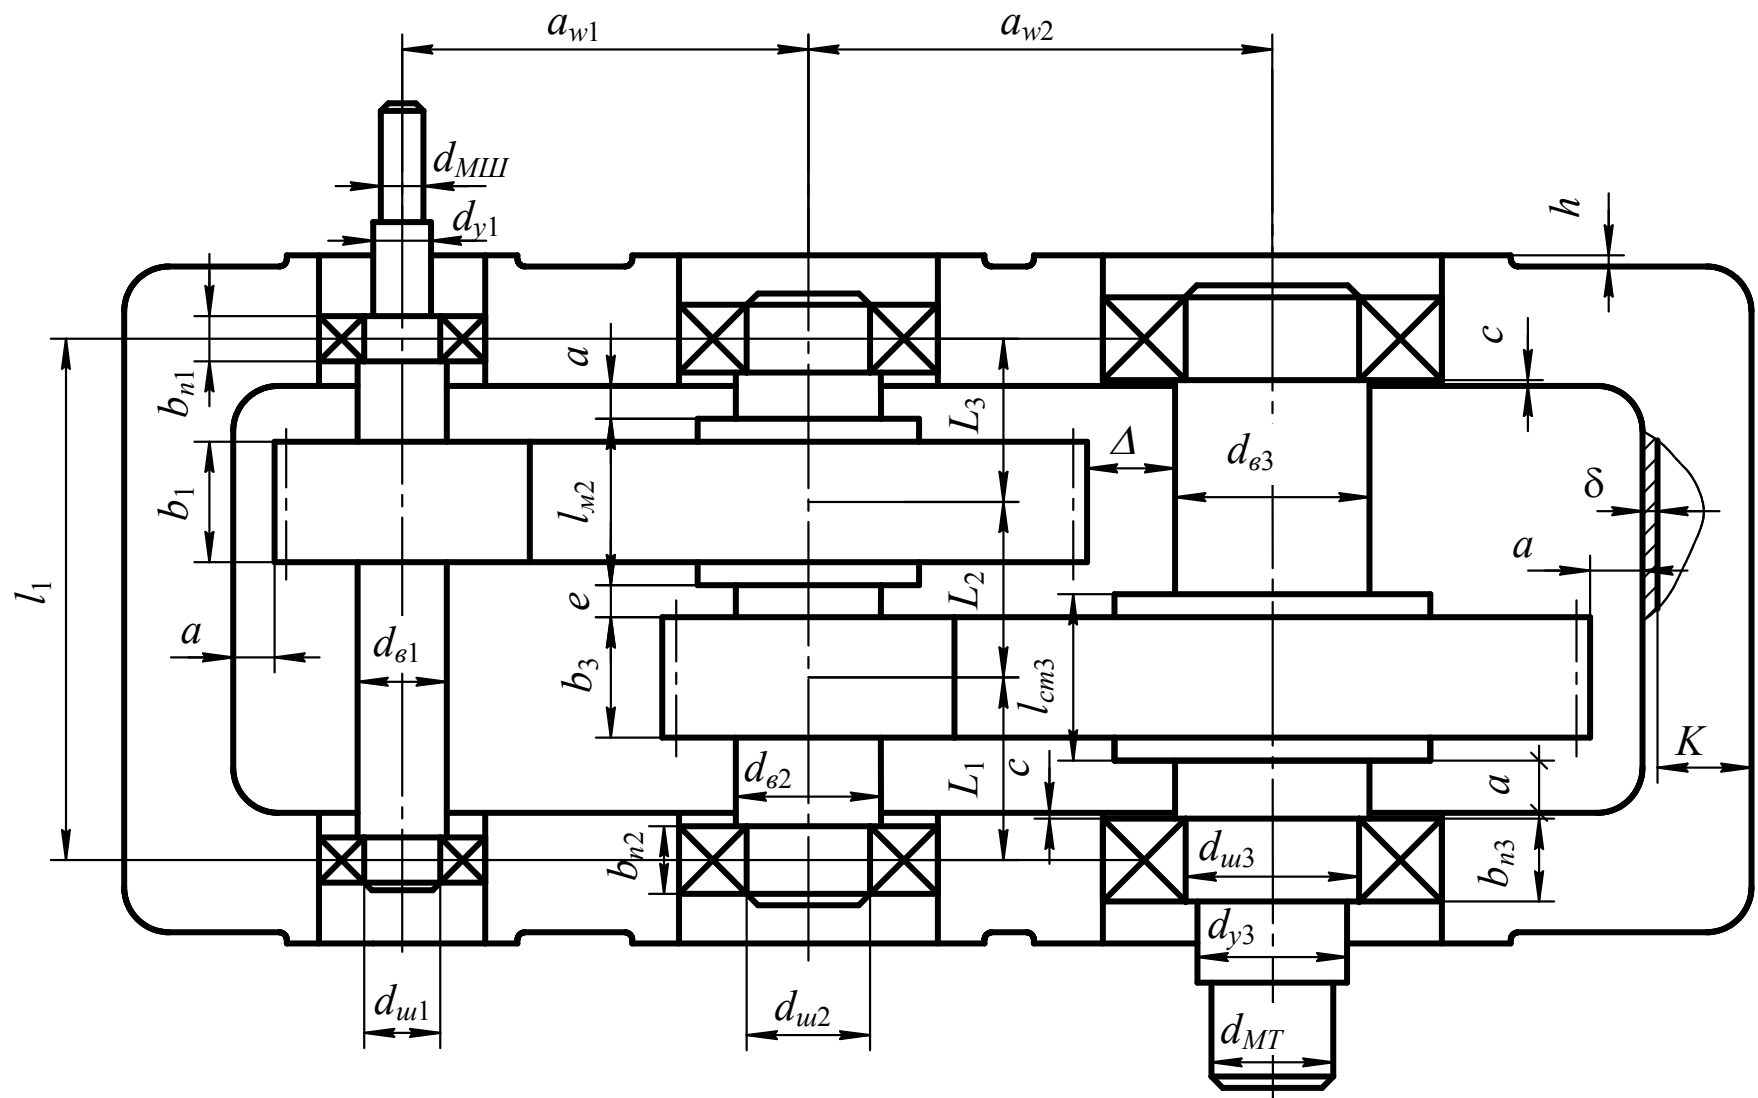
Эскизная компоновка двухступенчатого цилиндрического редуктора
